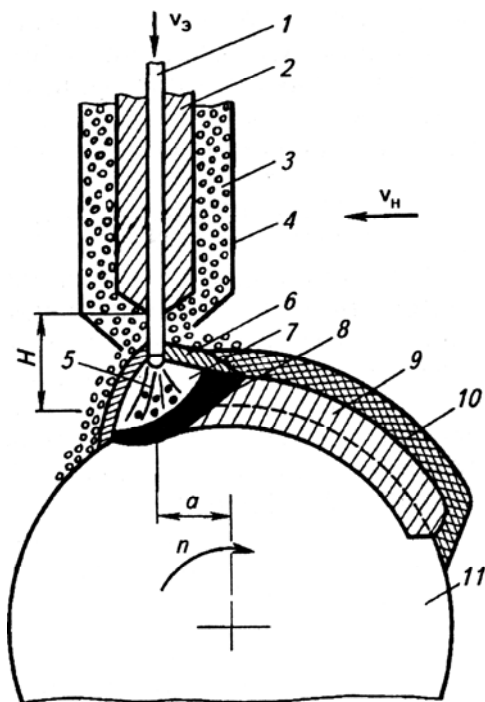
Схема наплавки под слоем флюса цилиндрических деталей:
